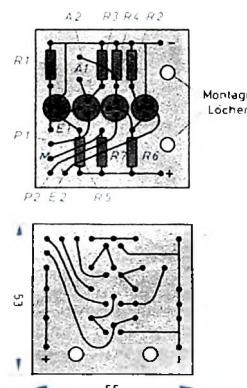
Oben: Auslegung der gedruckten Schaltung mit Bauteilen, unten: ohne Bauteile (in dieser Form wird die Auslegung auf die Platinе geklebt)
